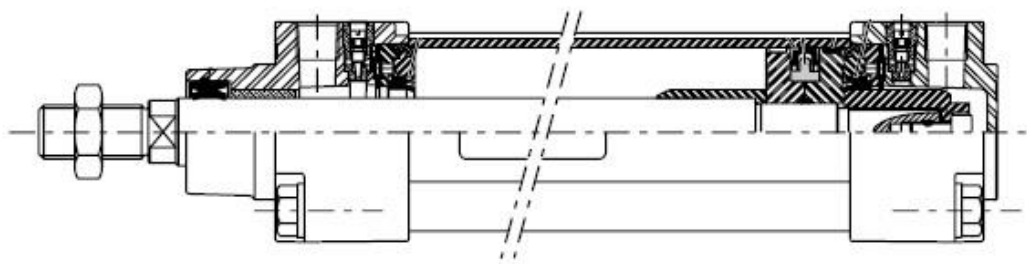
Desenho de conjunto do atuador pneumático [8].
